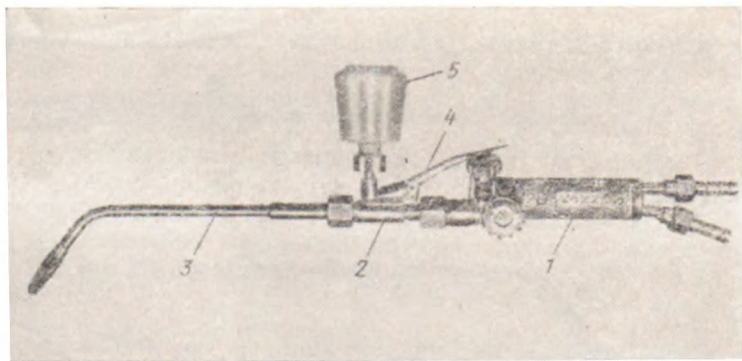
Горелка ГАЛ-2-68 для наплавки деталей самофлюсующимися порошковыми сплавами
